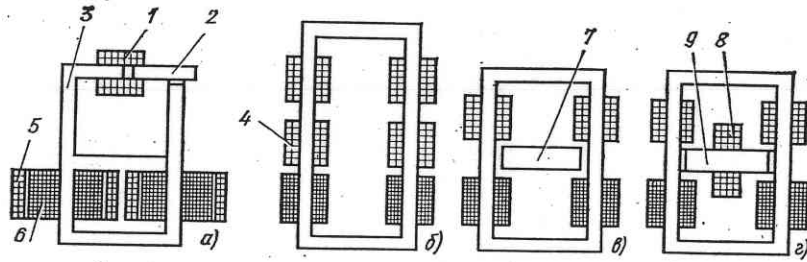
Основные конструктивные схемы сварочных трансформаторов: а — тип СТН и ТСД; б — тип ТС и ТД; в — тип СТП; г — тип ТДФ; 1 — обмотка дросселя; 2 — подвижный сердечник дросселя; 3 — магнитопровод дросселя и трансформаторов; 4 — подвижная вторичная обмотка трансформатора; 5, 6 — первичная и вторичная обмотки; 7 — подвижный магнитный шунт; 8 — обмотки управления; 9 — неподвижный магнитный шунт
